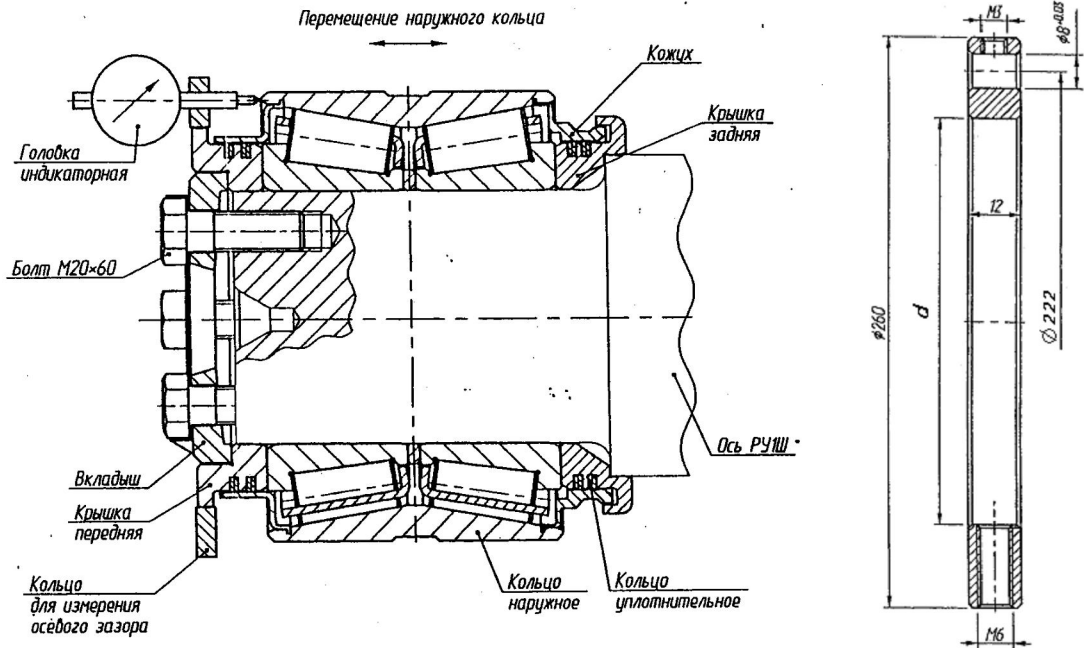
Схема измерения осевого зазора подшипника в габаритах 130x230x150 мм и эскиз кольца для установки индикатора часового типа
